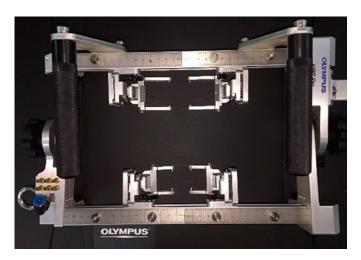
Distintas aplicaciones del OmniScan MX2. Escáner con TOFD para inspección de soldadura en tuberías.
